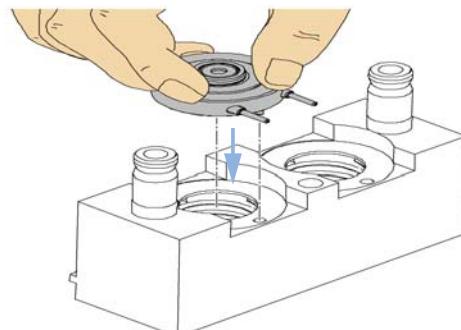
Insertion des bagues supports de l'accessoire de rinçage de joint en continu.
